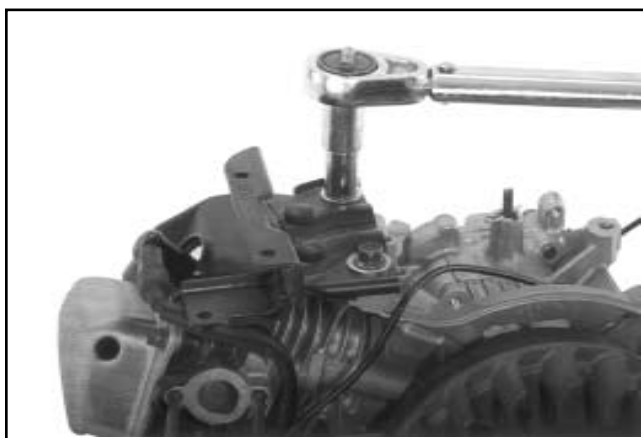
CS6 e CS4. Montaggio del supporto del serbatoio del carburante di sinistra.
